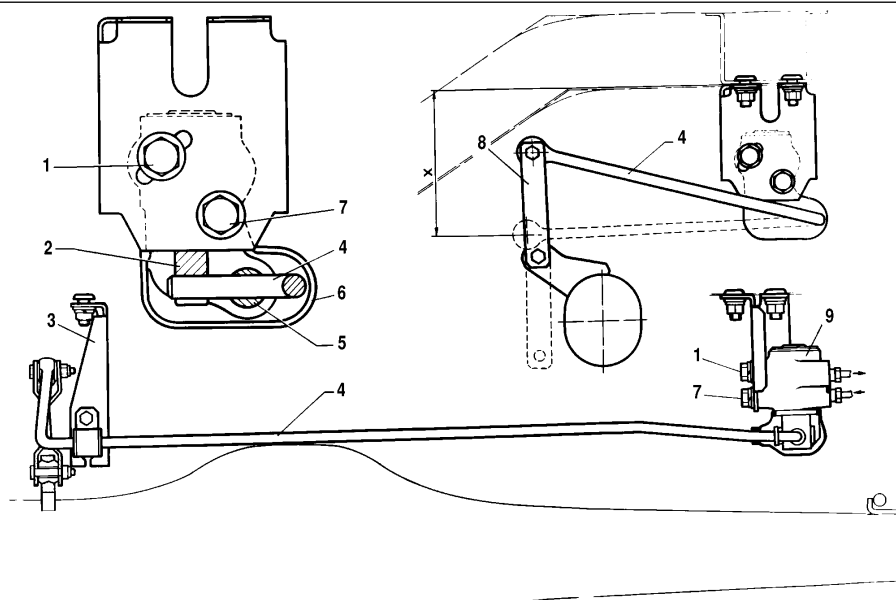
Schéma d'installation du régulateur de pression de frein arrière et de réglage :
